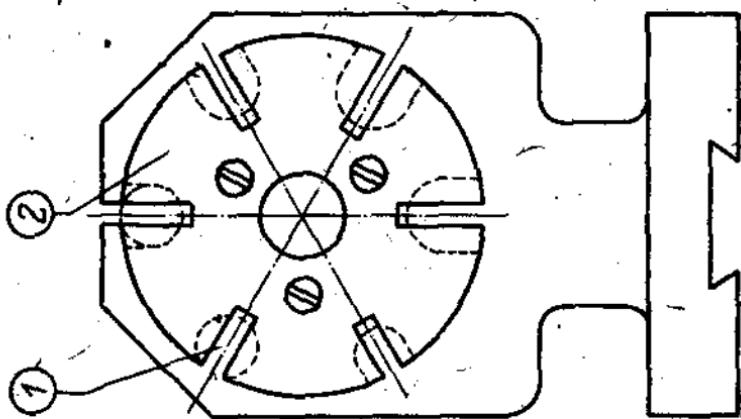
Приспособление к фрезерному станку для изготовления шпонок Вудруфа.
